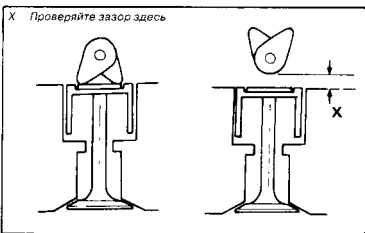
Расположение кулачков распределительного вала для проверки тепловых зазоров клапанов
